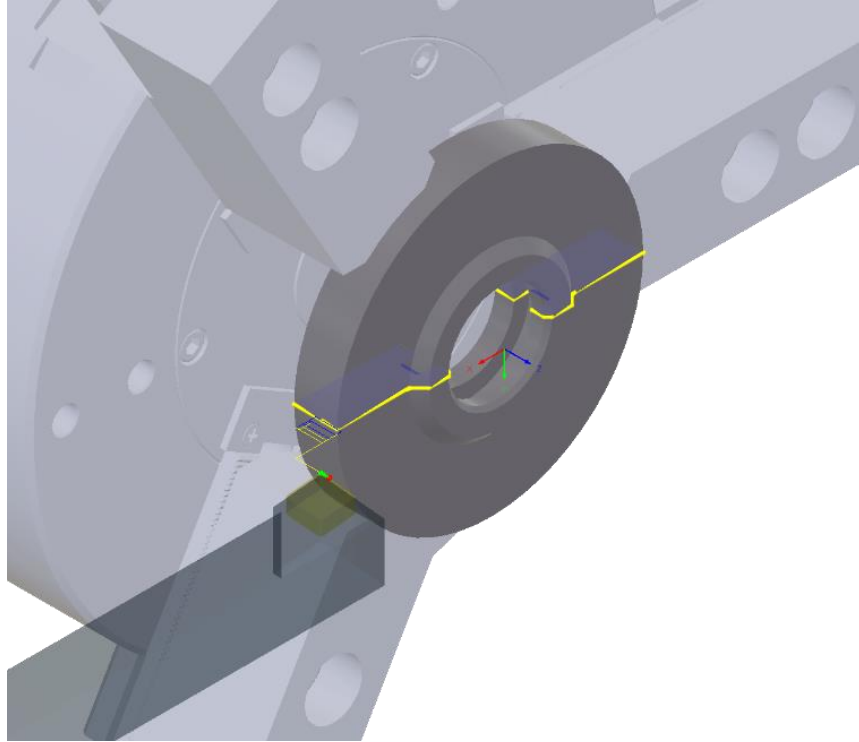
Зображення переходу точіння зовнішньої поверхні заготовки
